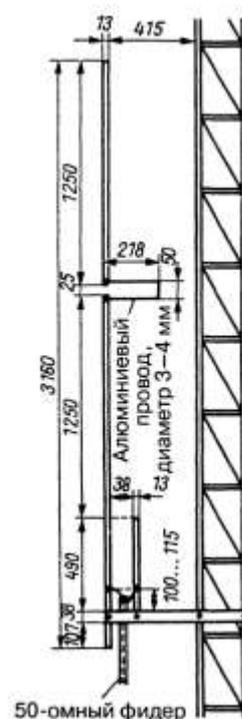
Устройство и размеры удлиненного двойного «Цеппелина», рассчитанного на двухметровый диапазон и установленного перед решетчатой мачтой
